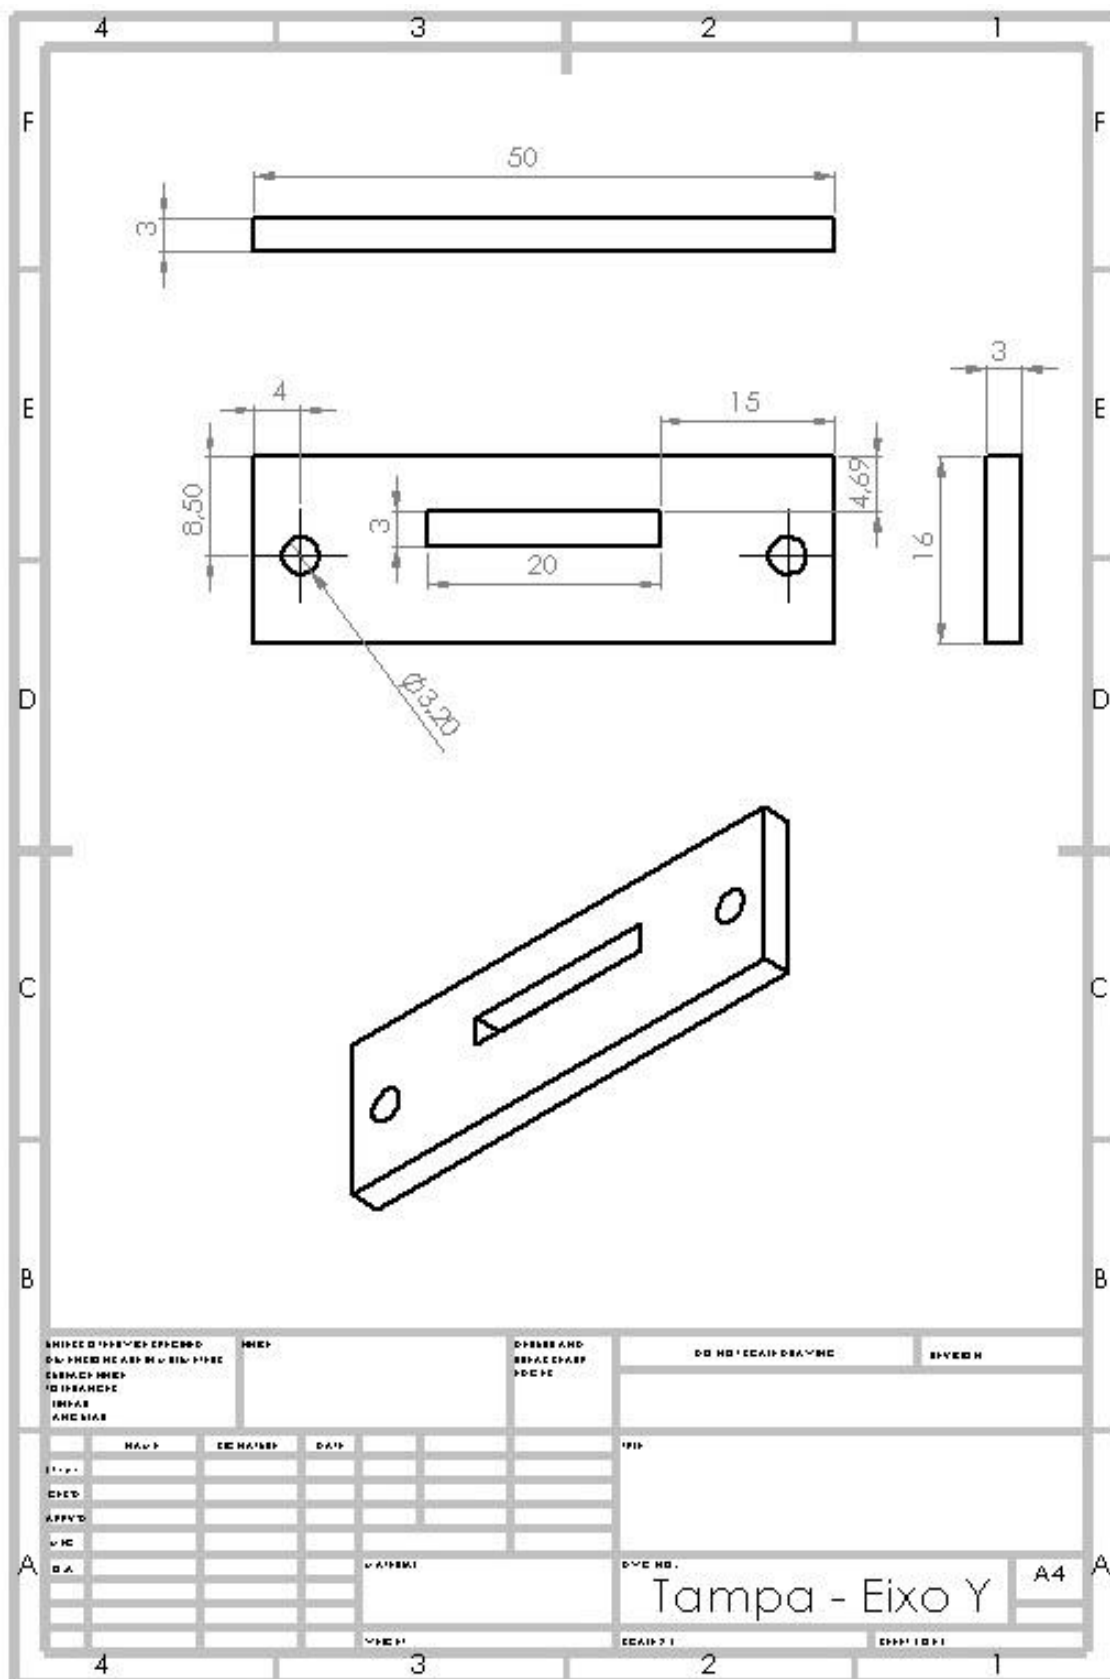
Desenho técnico da peça Tampa - Eixo Y.
